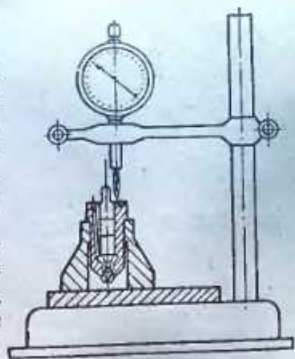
Подставка ЛМ9589-137 для проверки подъема иглы
